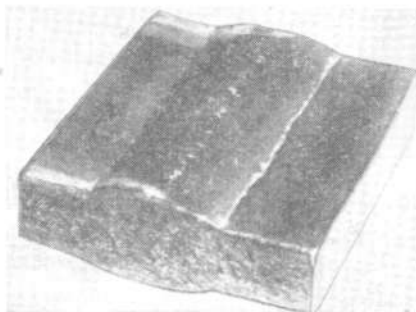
Внешний вид шва, выполненного автоматической сваркой под флюсом.
